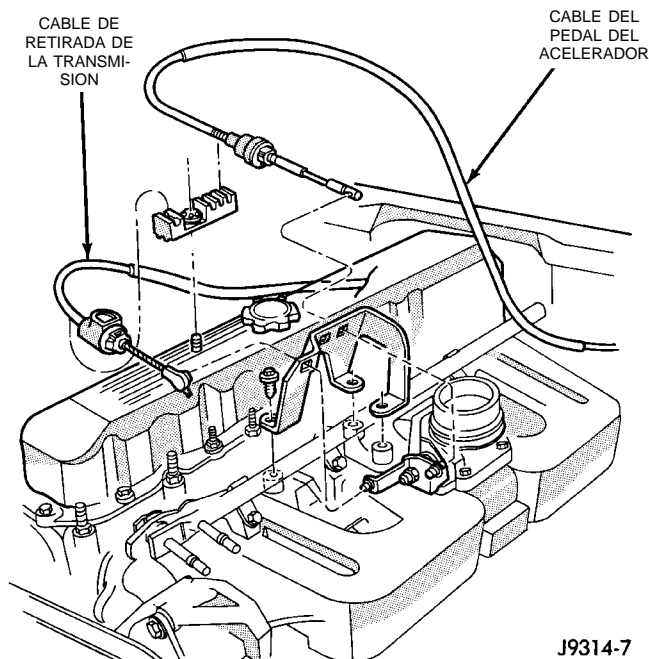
Recorrido del cable de mariposa—Motor de 4.0L
